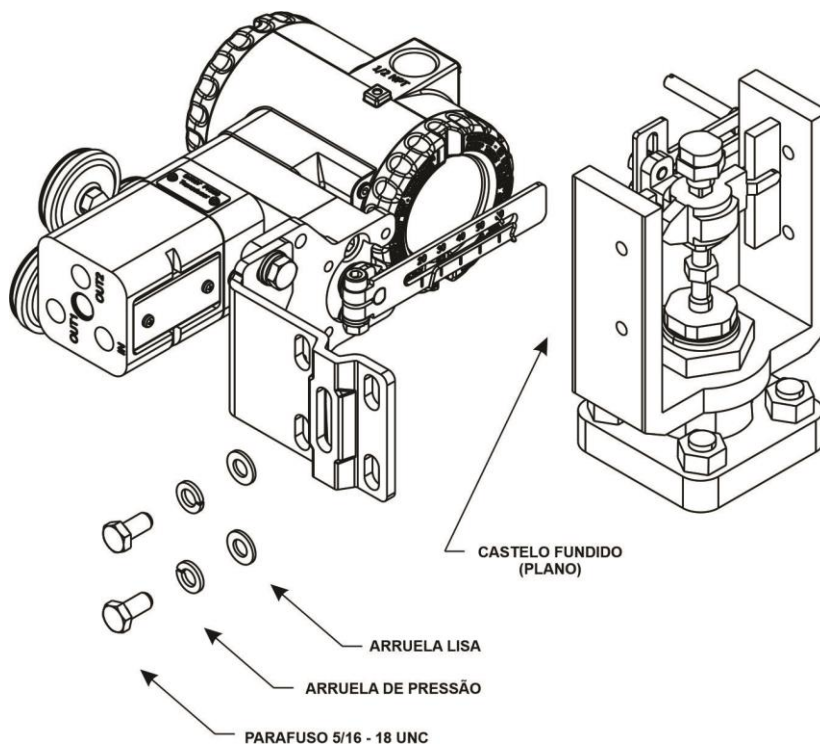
Fixação do suporte de montagem em castelo fundido com superfície plana
